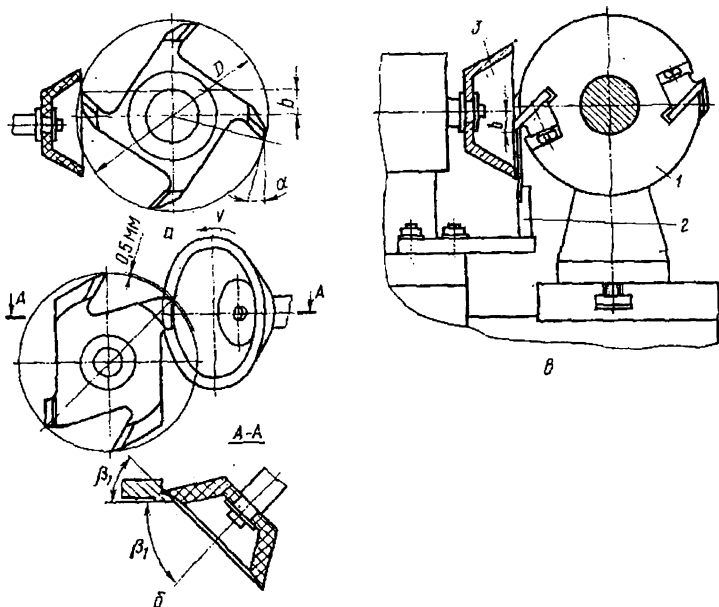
Схемы заточки зубьев фрез по задней поверхности:
